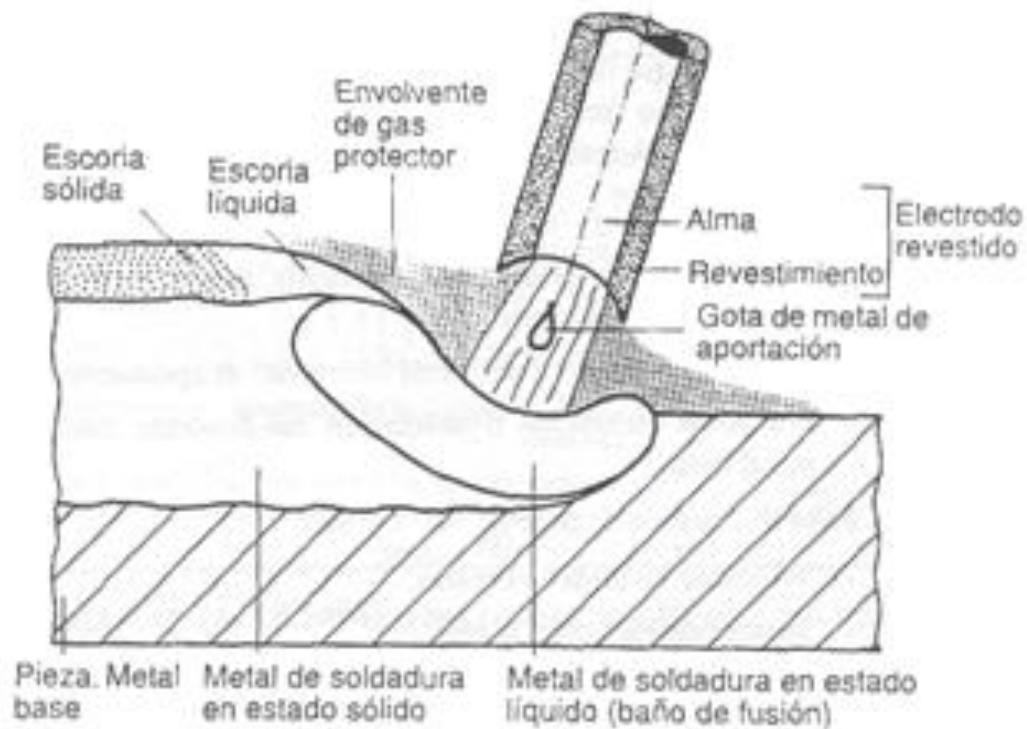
Principio de operación soldadura SMAW (Figura tomada del "Instituto Argentino de Siderurgia")
